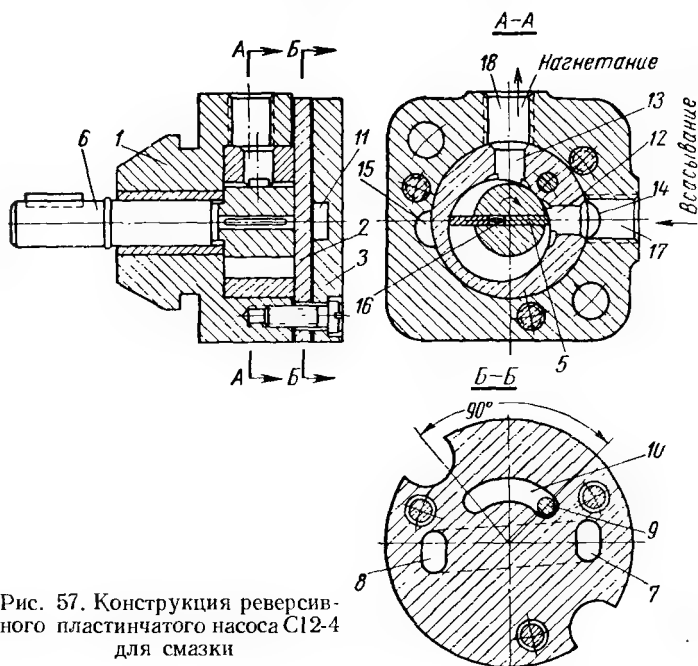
Конструкция реверсивного пластинчатого насоса С12-4 для смазки
